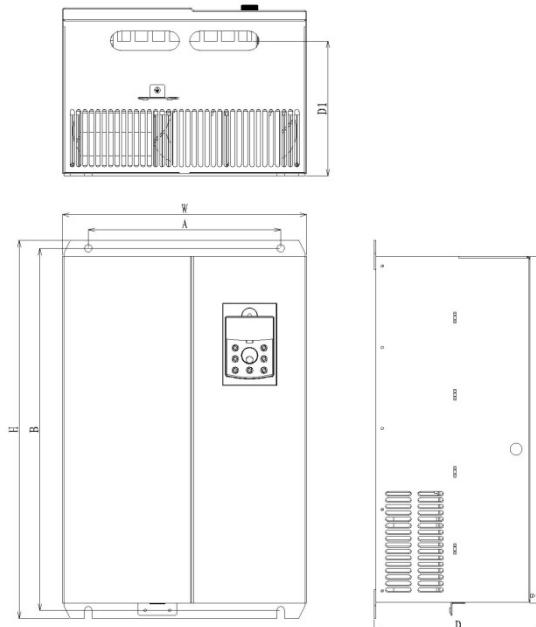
Габаритные и монтажные размеры корпуса преобразователя из металла.
